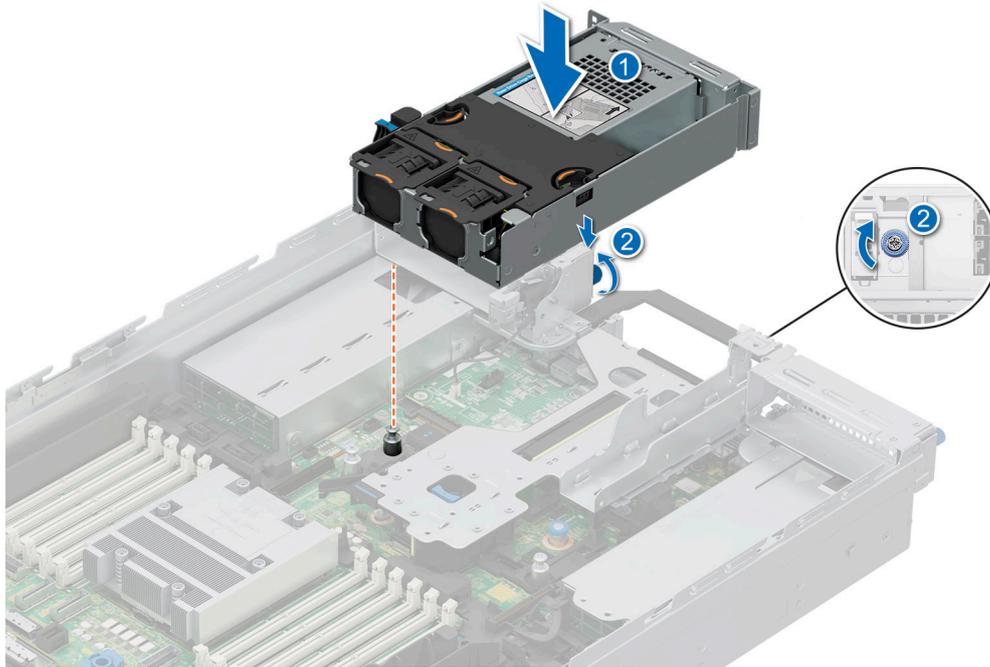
Installation du module de disques arrière 2 x 2,5 pouces
